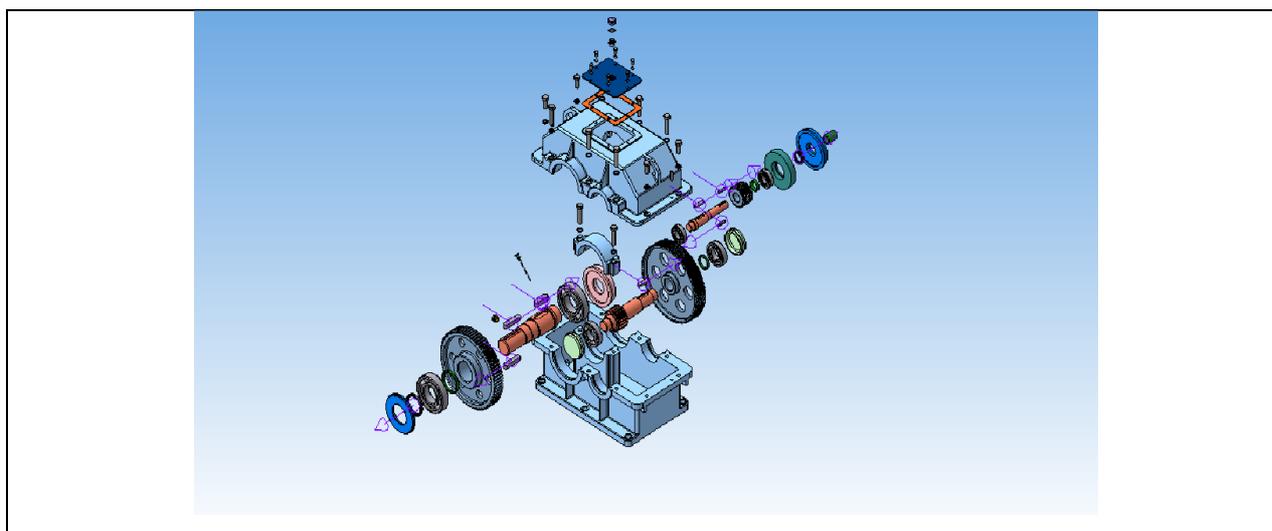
Разобранный двухступенчатый цилиндрический соосный редуктор
